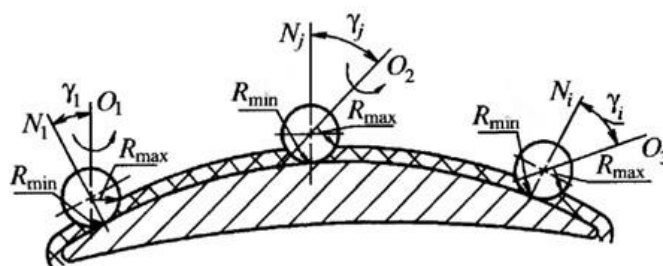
схема положень інструмента з радіусною ріжучою поверхнею на поверхні заготовки.
